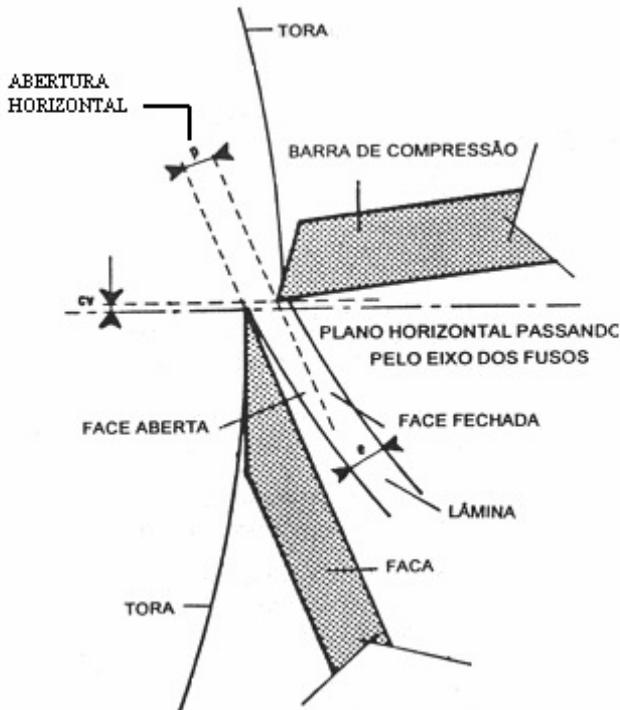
Seção transversal de um torno, mostrando a relação geométrica entre as principais partes do corte da lâmina.
